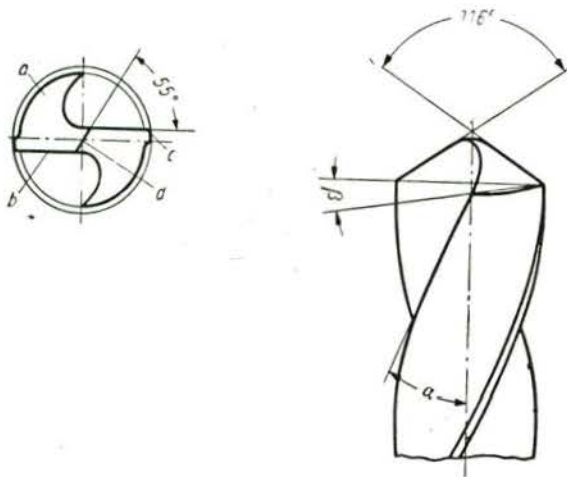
Winkel und Bezeichnungen am Spiralbohrer
